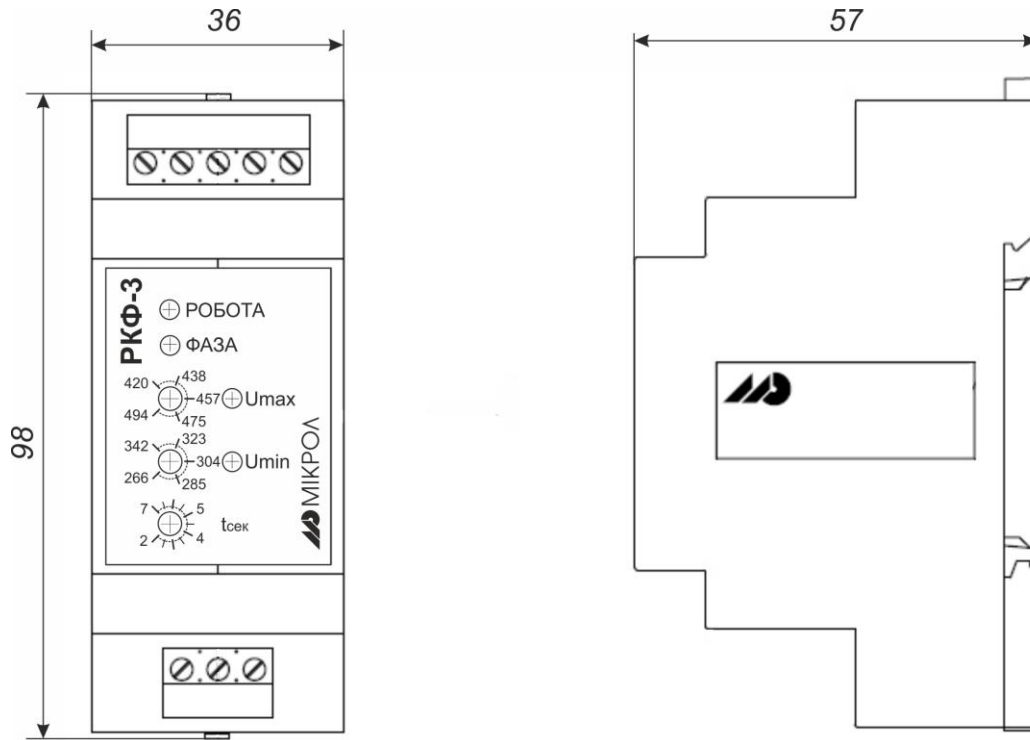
Зовнішній вигляд і габаритні розміри реле контролю фаз РКФ-3
